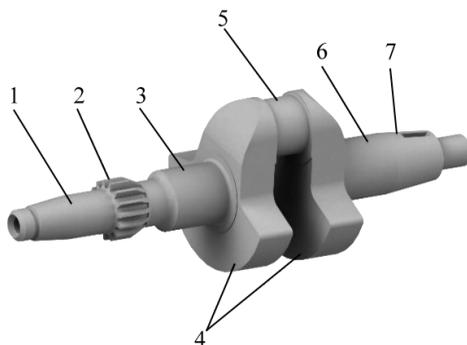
Общий вид коленчатого вала проектируемого двигателя:
